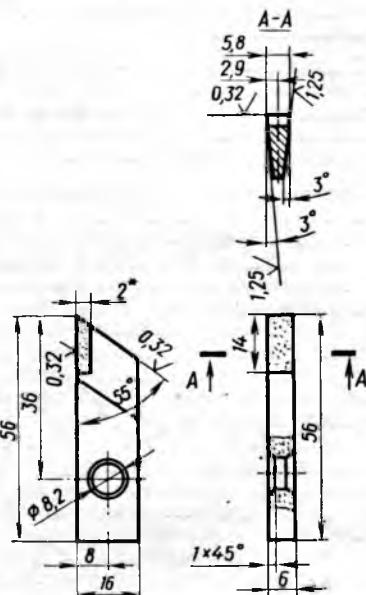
Резец (сталь марки 45 ГОСТ 1050—60)
